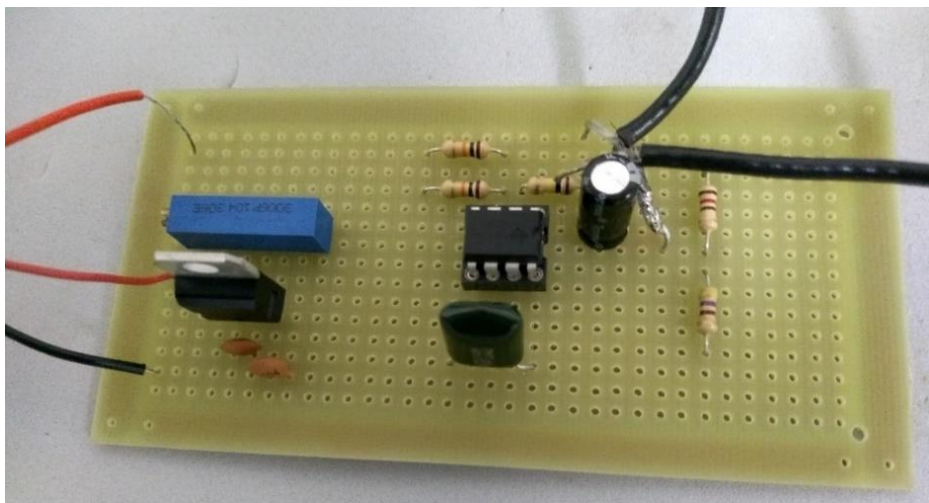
Protótipo de componentes montado e soldado em uma placa de fenolite perfurada. Fonte: o próprio autor (2019)
